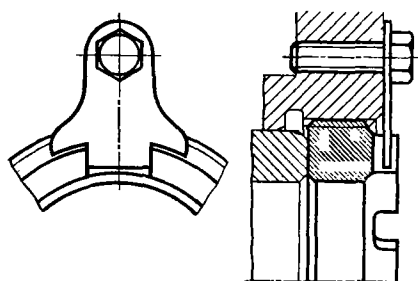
Стопорение внутренней гайки с торцовым зубом при помощи привернутой пластинки
